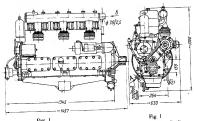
Общий вид двигателя 6Ч 10,5/13
